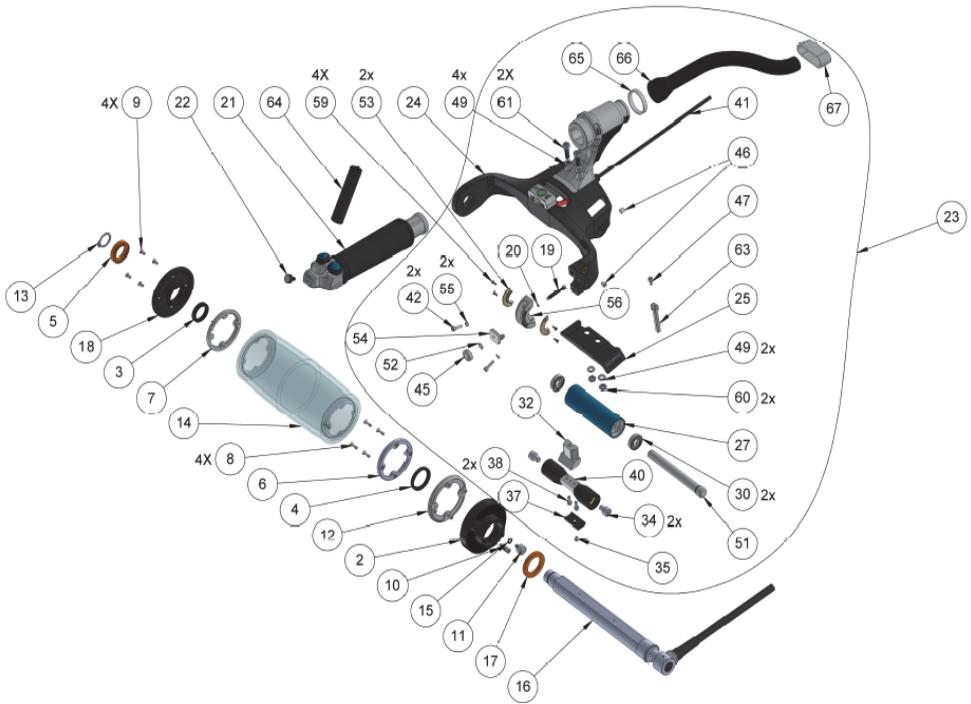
RollerFORM XL – Übersicht der Ersatzteile 1
